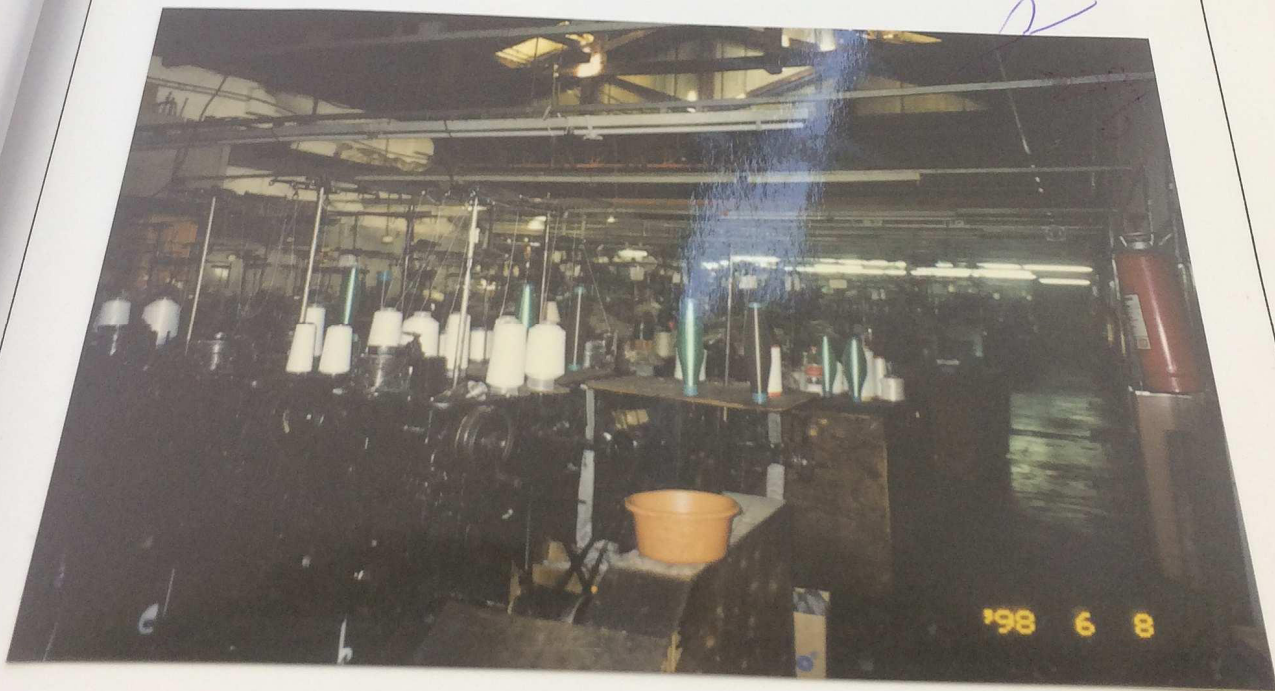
Vista parcial das áreas da edificação No. 1 do imóvel avaliando.
